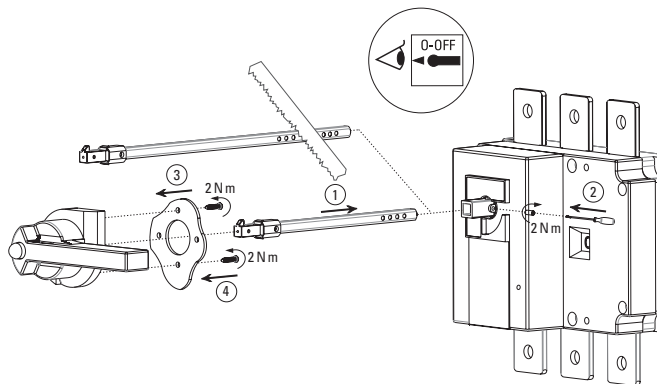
а – Порядок монтажа выносной ручки для рубильников 160-630 А
